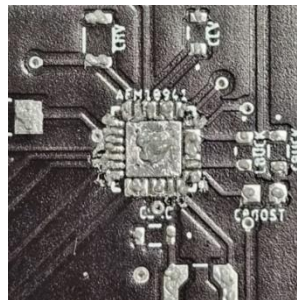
Pasta de Soldadura en *Pads* del chip AEM10941
